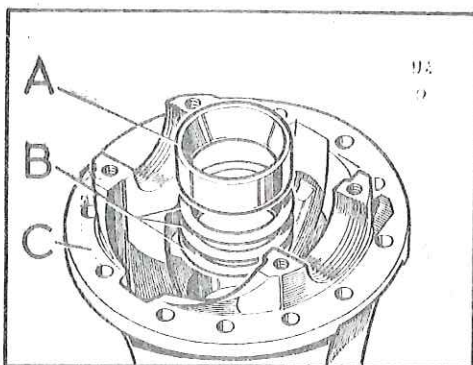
Pista exterior del cojinete de extremo del piñón
